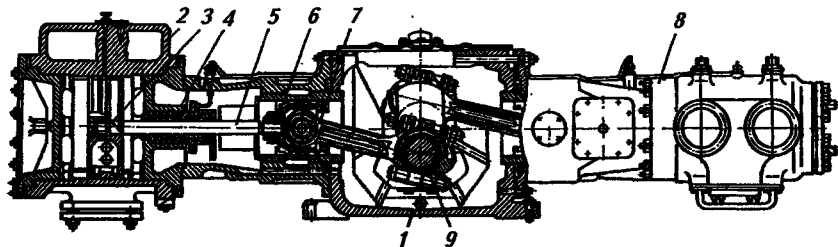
Аммиачный оппозитный двухступенчатый компрессор:
